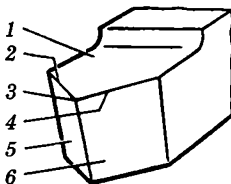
Конструктивные элементы режущей части токарного резца:
